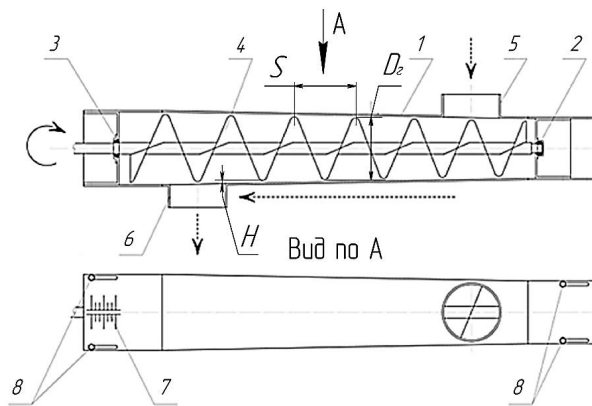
Шнековий транспортер з регульованим зазором H : 1 – кожух; 2, 3 – підшипникові вузли; 4 – конусний гвинтовий робочий орган; 5 – завантажувальний пристрій; 6 – розвантажувальний пристрій; 7 – шкала регулювання зазору; 8 – механізми переміщення гвинтового робочого органу; S – крок гвинта; D_e – діаметр гвинта
